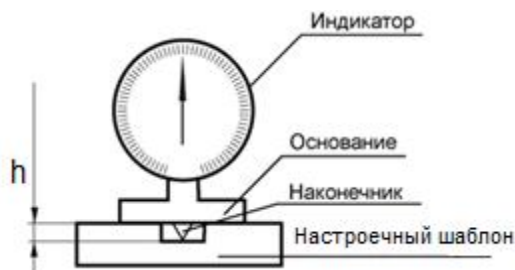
Схема настройки прибора для измерения высоты профиля резьбы
